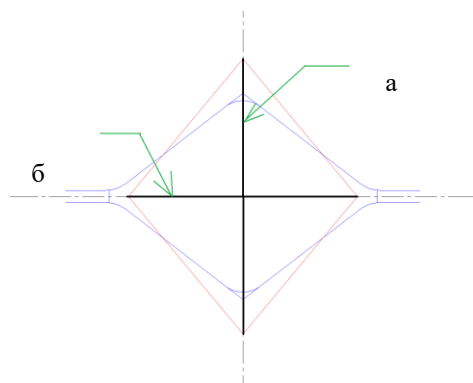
Несовпадение малой (б) и большой (а) диагоналей заготовки и калибра
